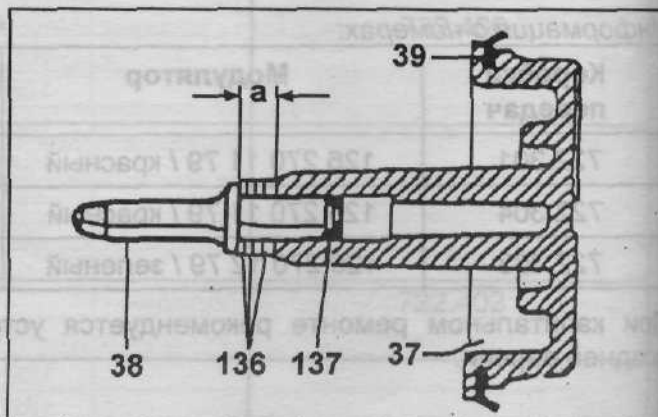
37 - Поршень ленточного тормоза В1; 38 - Шток; 39 - Уплотнение; 136 - Прокладки; 137 - Кольцевое уплотнение.
